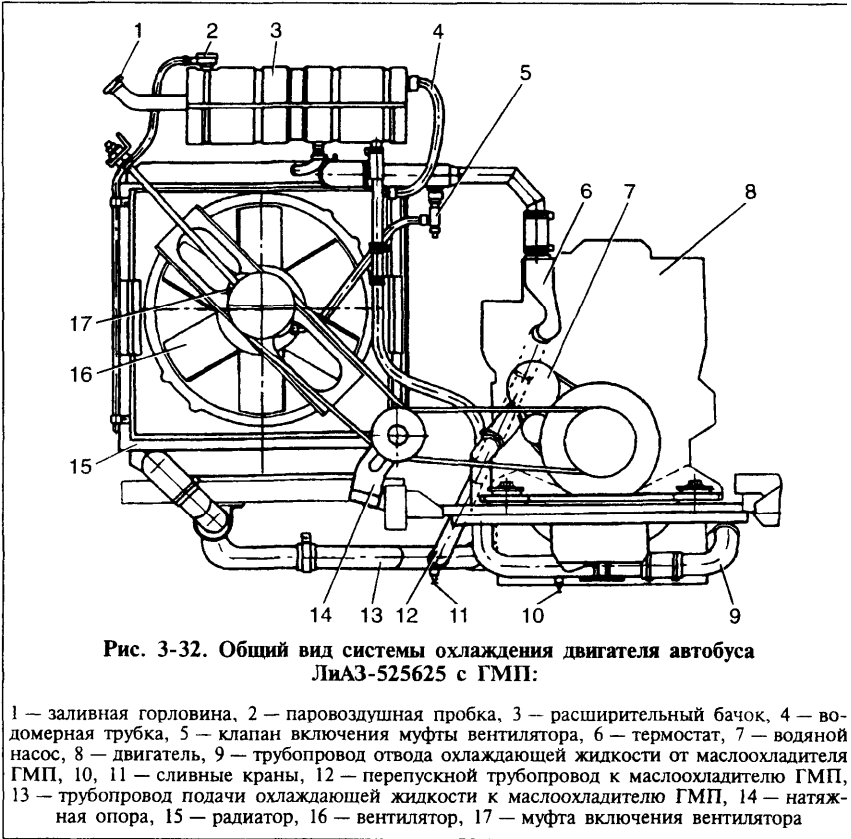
Общий вид системы охлаждения двигателя автобуса ЛиАЗ-525625 с ГМП:
